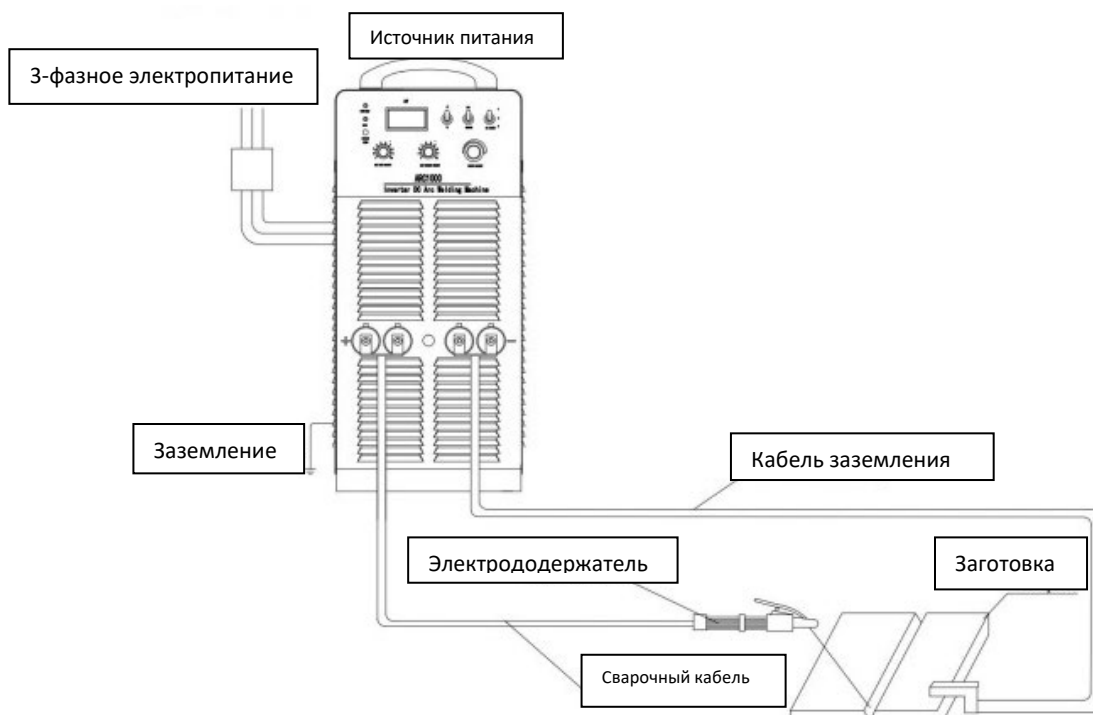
Установка процесса ручной дуговой сварки покрытым электродом
